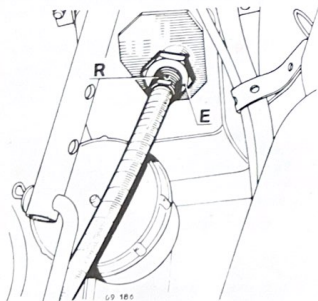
Cable de mando del embrague en su tope soporte.
